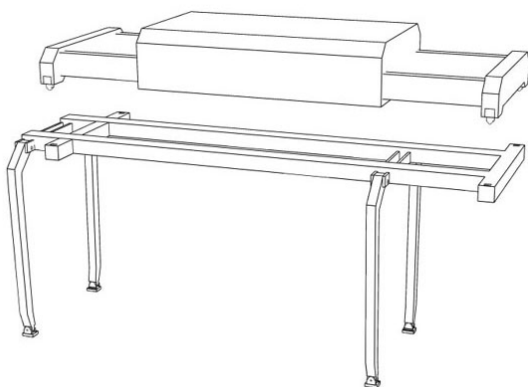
H-5.15.I – Telaio rettangolare connesso allo *spreader*. Fonte: [50]
